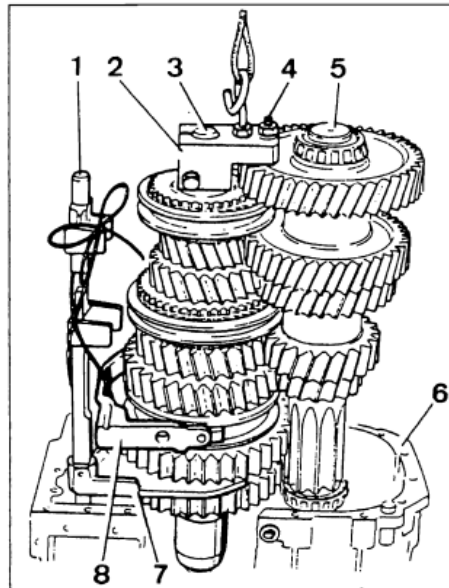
Виймання вторинного та проміжного валів із картера коробки передач:
